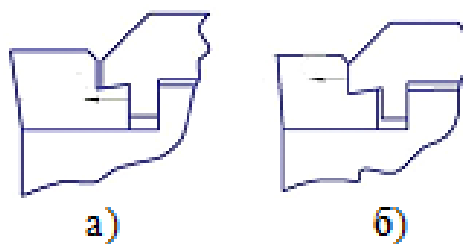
Схеми базування різальних пластин по упорній поверхні:
